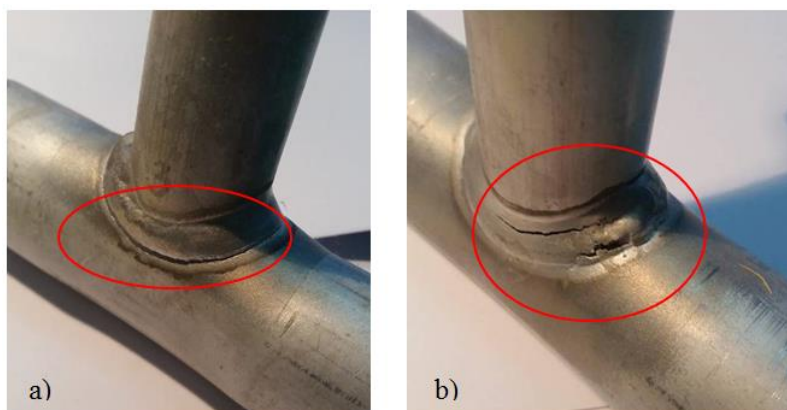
a) Fratura na ZTA do provete 26 e b) fratura no cordão de soldadura do provete 20.
